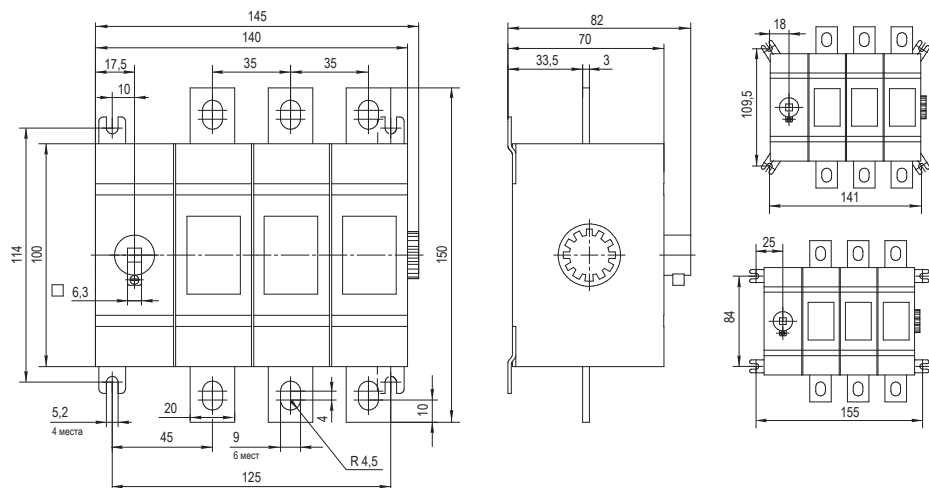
Выключатель-разъединитель 160 – 250 А стандартного исполнения
